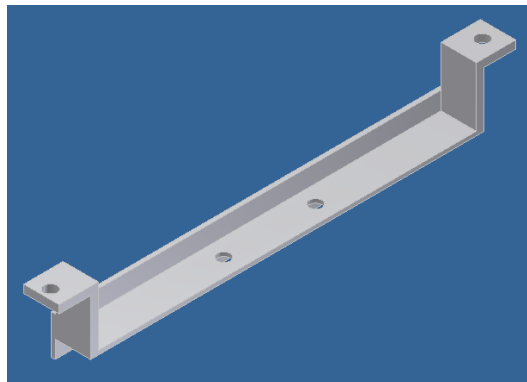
4. 5. 2. Tee sección C y platinas soldadas
